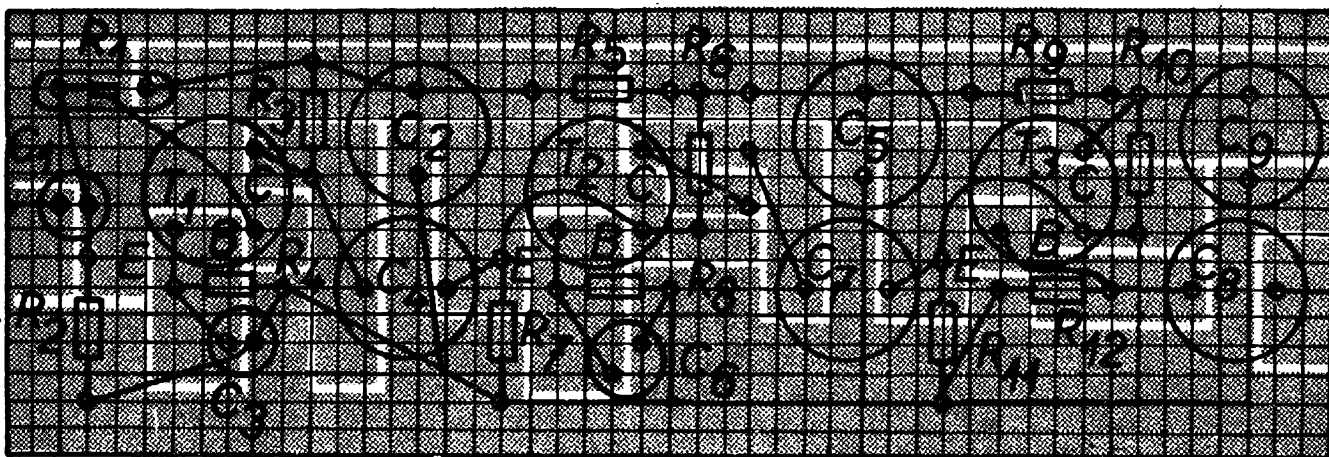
Obrazec plošných spojů vytvořený soustavou spojových čar
